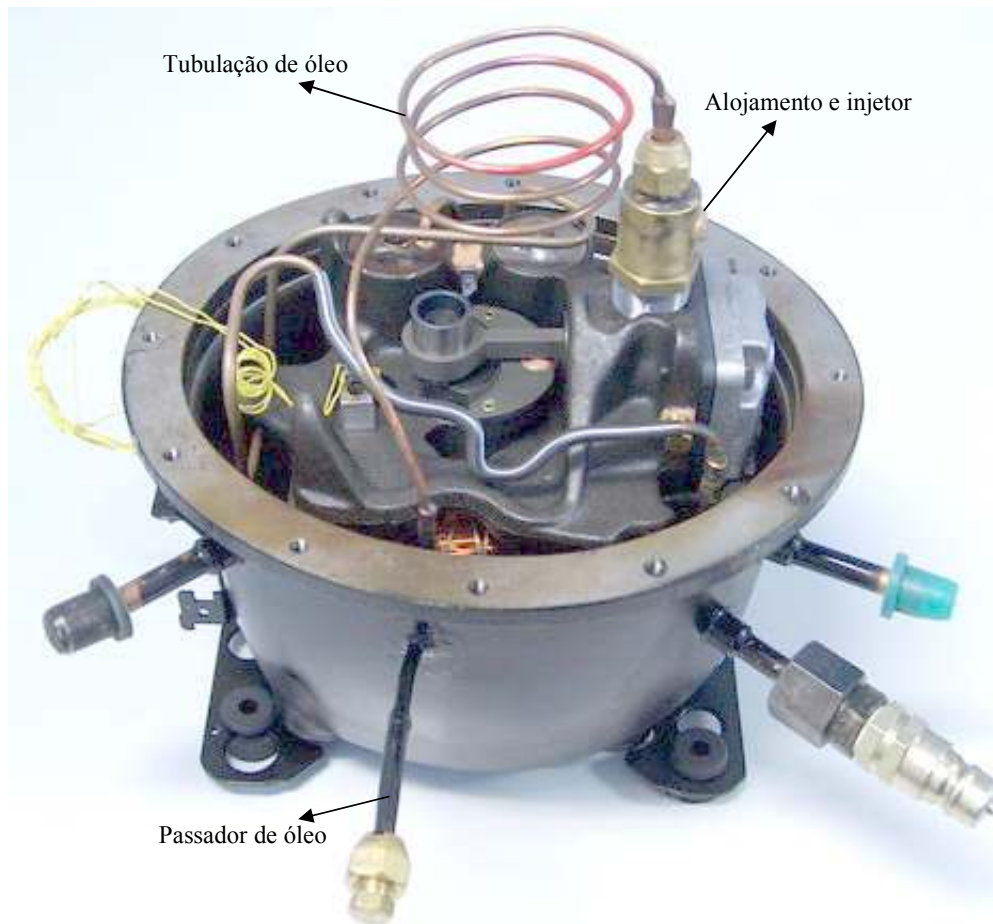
Compressor com o injetor, passador e linha de óleo.
